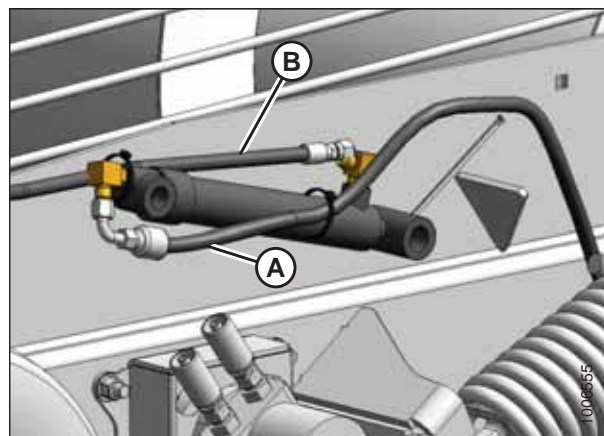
Главный гидроцилиндр — Левая сторона жатки
